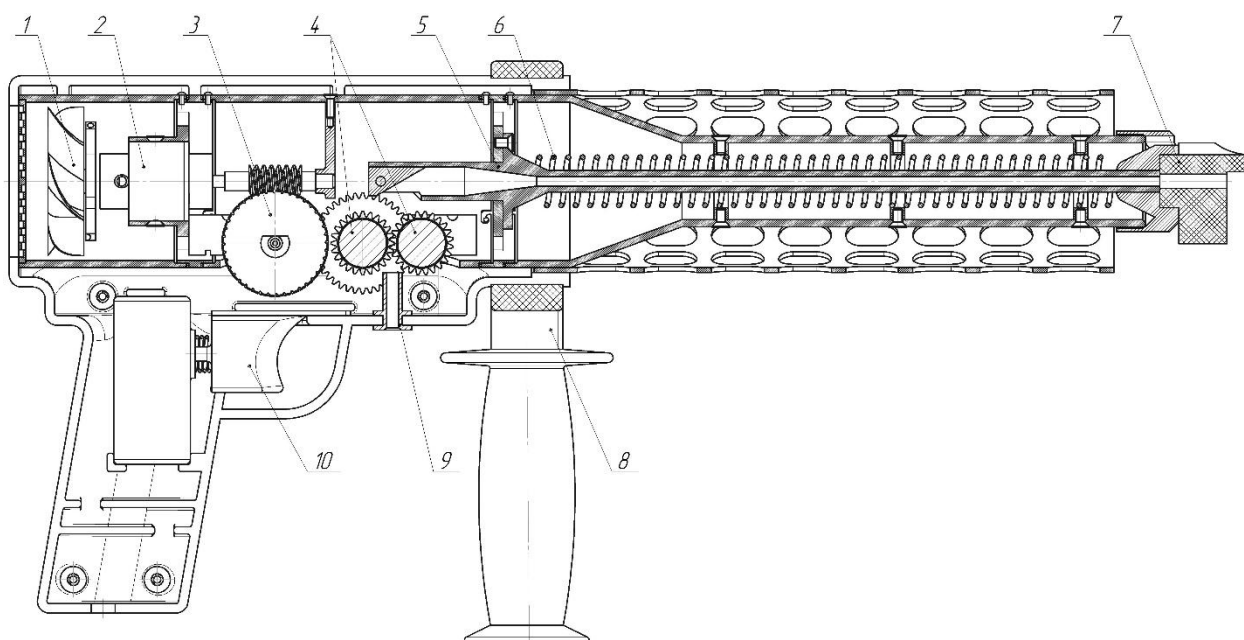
Пояснительная схема сварочного экструдера.
